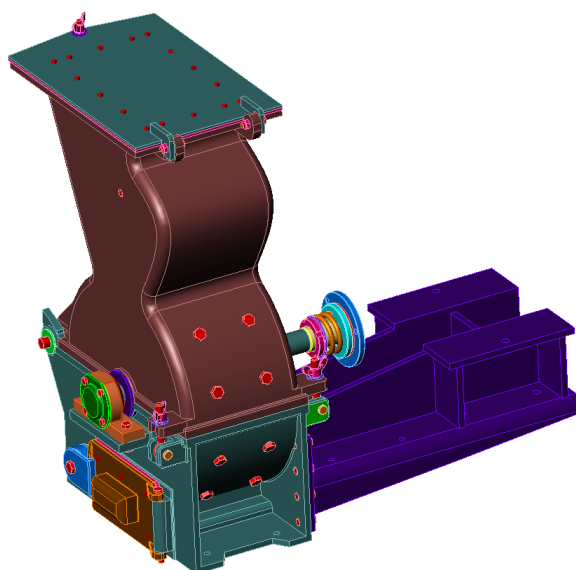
Общий вид разработанной конструкции молотковой дробилки
